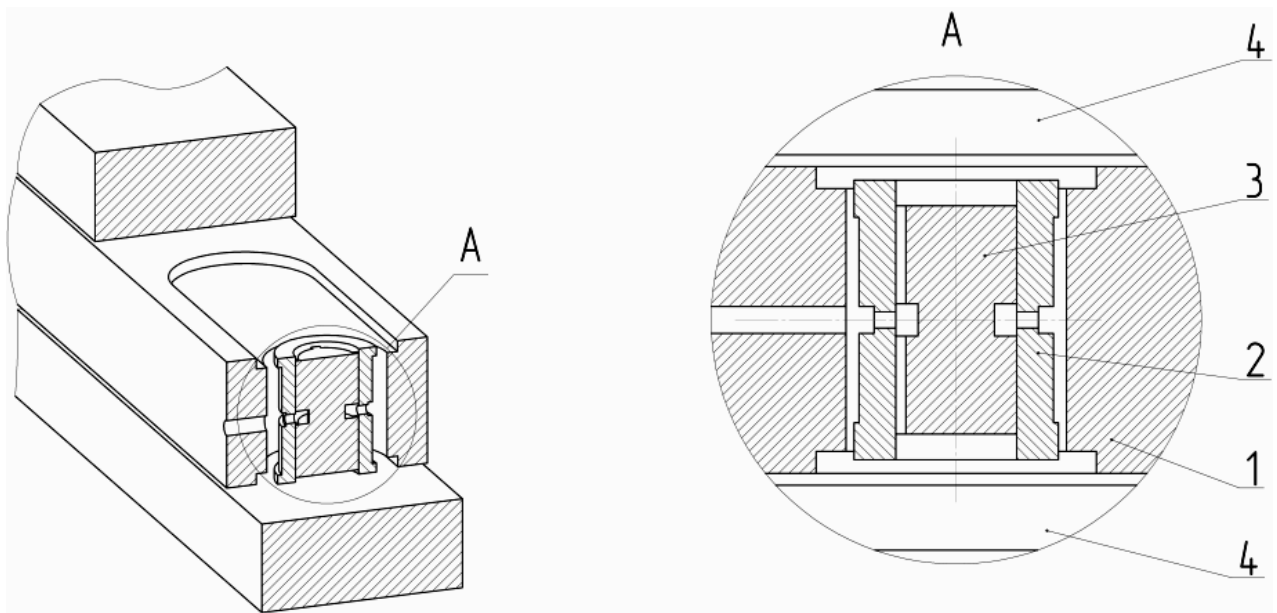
Замкнутые адаптивные гидростатические направляющие с плавающими плунжерными регуляторами активного нагнетания смазки
